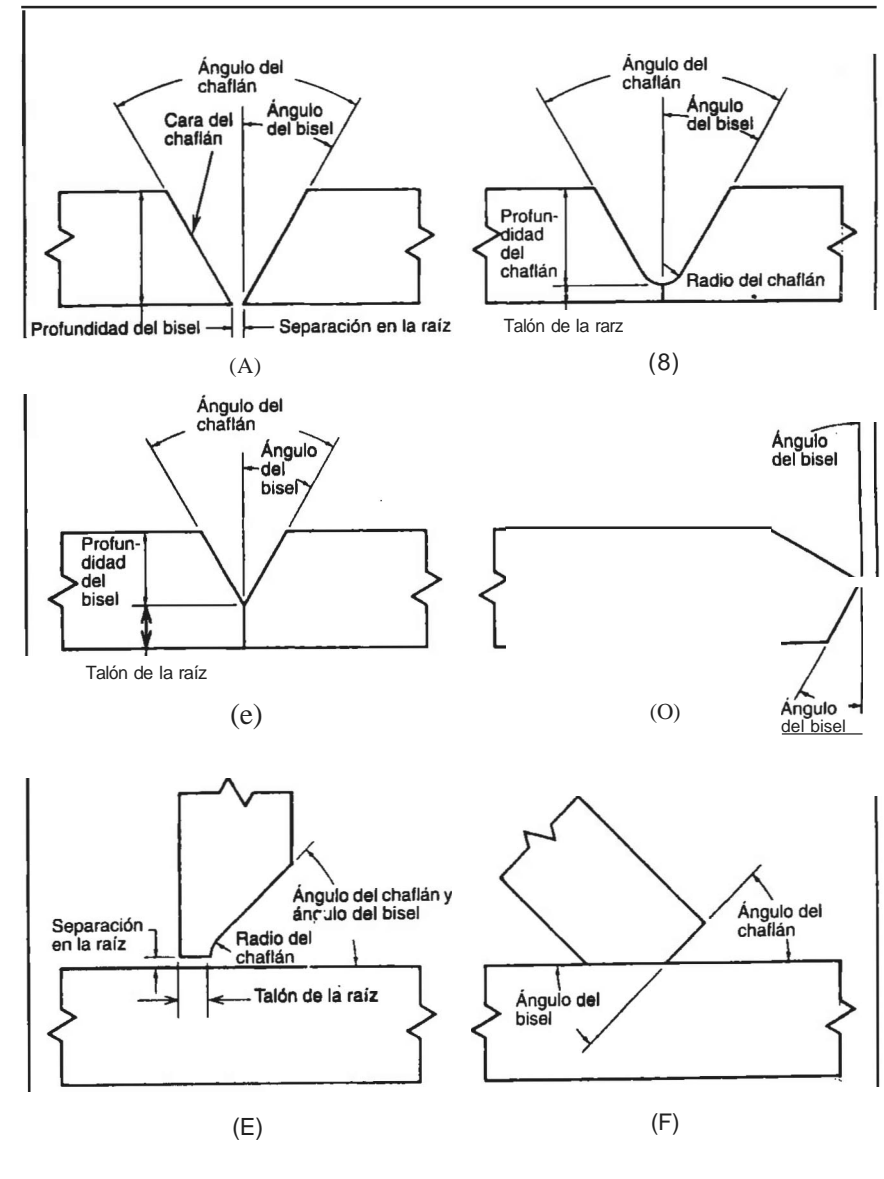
GEOMETRÍA DEL CHAFLÁN DE UNA SOLDADURA
